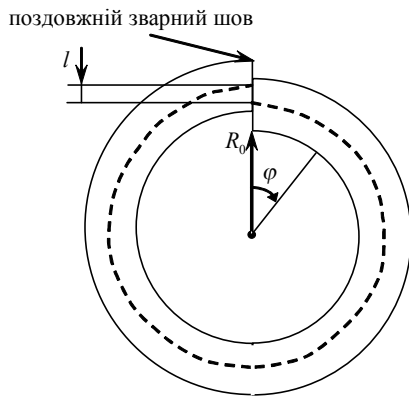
Поперечний переріз труби з осьювою неспіввісністю поздовжнього зварного шва
